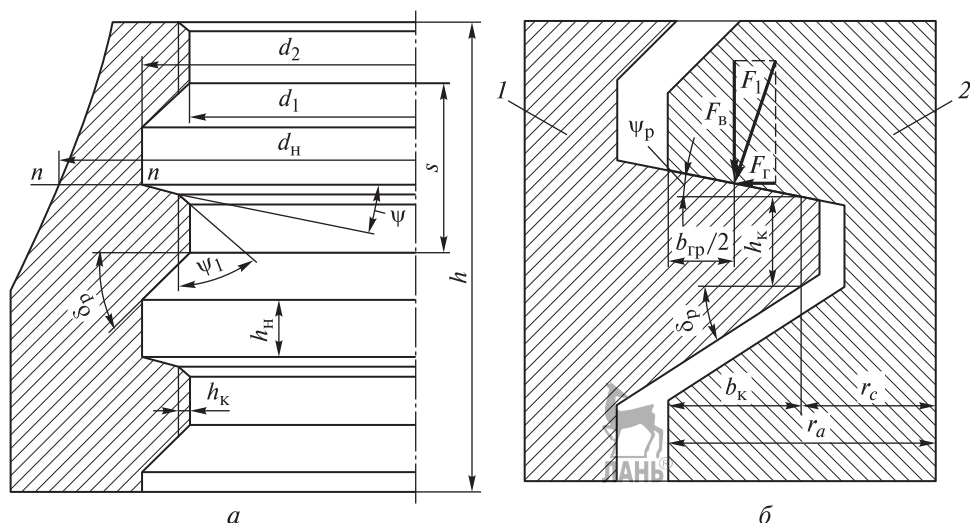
Профиль резьбовой гребенки сектора (а) и контакт зубцов гребенки сектора с зубцами корпуса (б):
